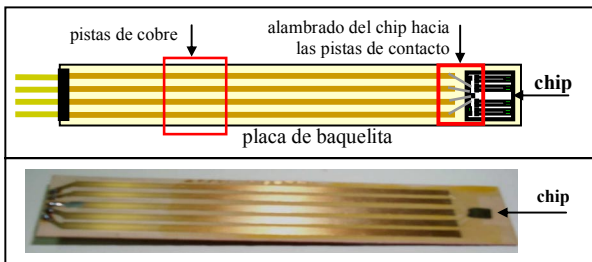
Montaje de un chip (4x4 mm) al circuito impreso.
